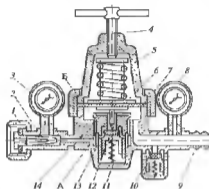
Одноступенчатый кислородный редуктор БКО-50: 1 — накидная гайка, 2, 13 — фильтры, 3, 8 — манометры, 4 — регулировочный винт; 5 — нажимная пружина, 6 — толкатель, 7 — мембрана, 9 — наплеватель, 10 — предохранительный клапан, 11 — запорная грузинка, 12 — регулирующий клапан, 14 — седло; А — камера высокого давления, Б — рабочая камера
